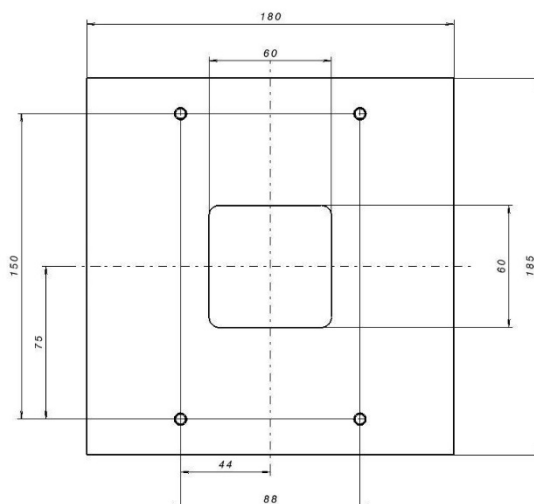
Bohrbild Standard-Adapterplatte BG D
